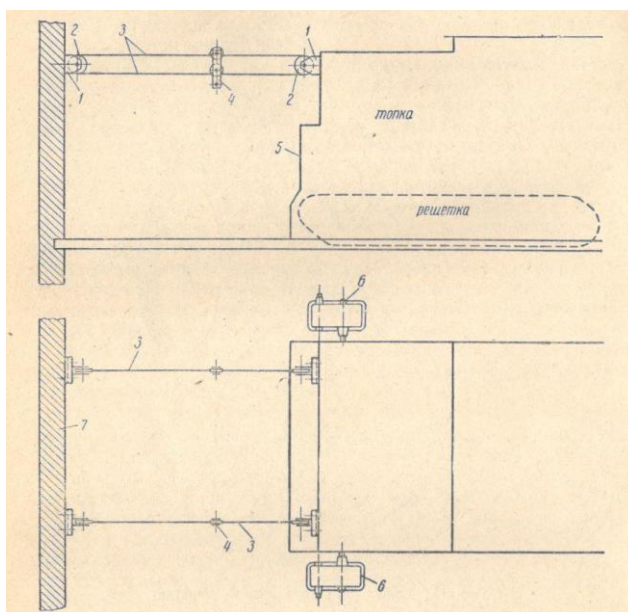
Канатные дорожки для ремонта цепной решетки
